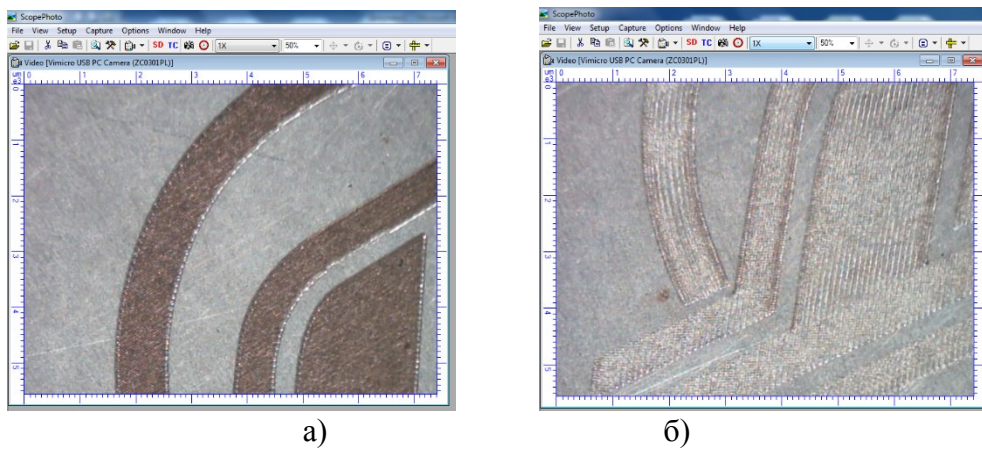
Рельєф поверхні при різних режимах обробки
